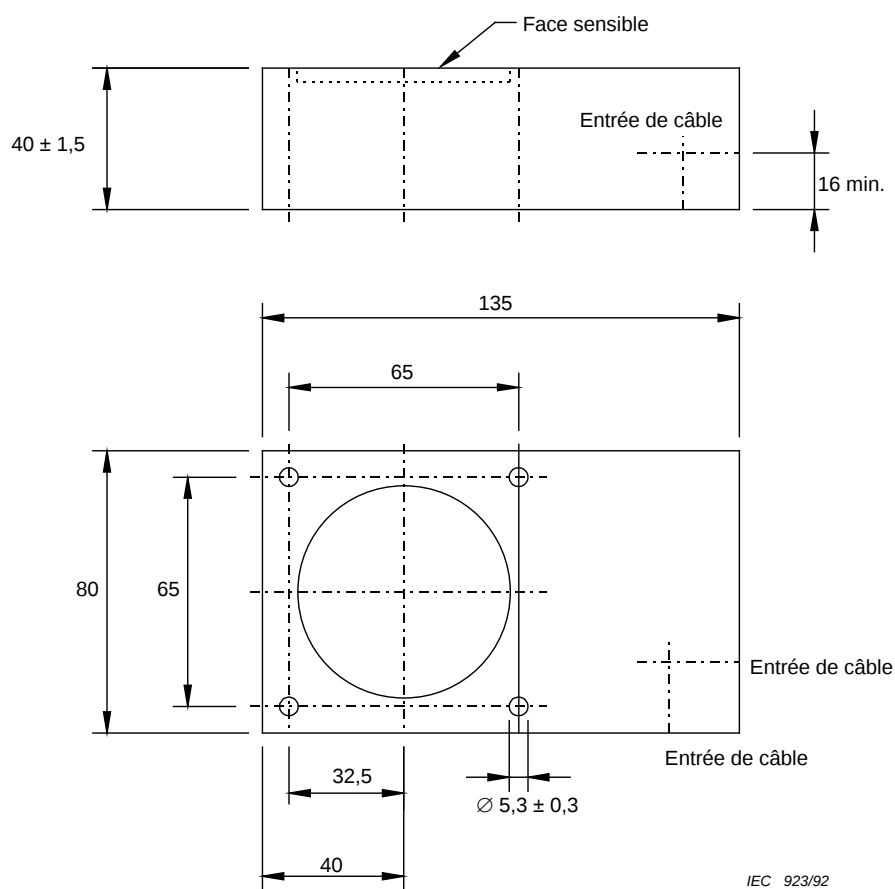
(UD) – Dimensions du type U3D80 en millimètres
